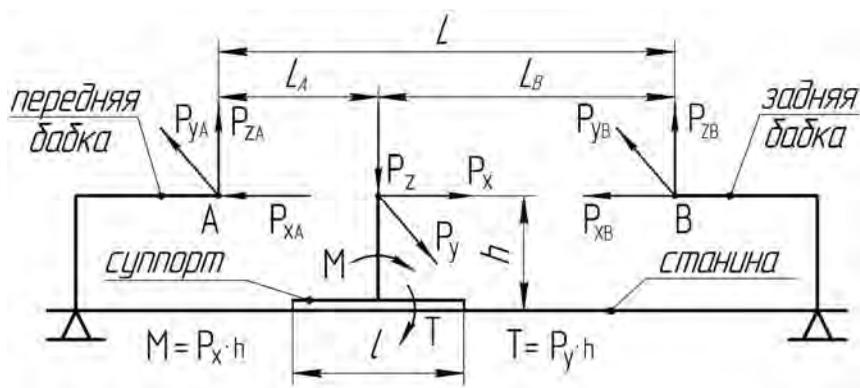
Расчетная схема действующих нагрузок на базовые детали токарного станка
